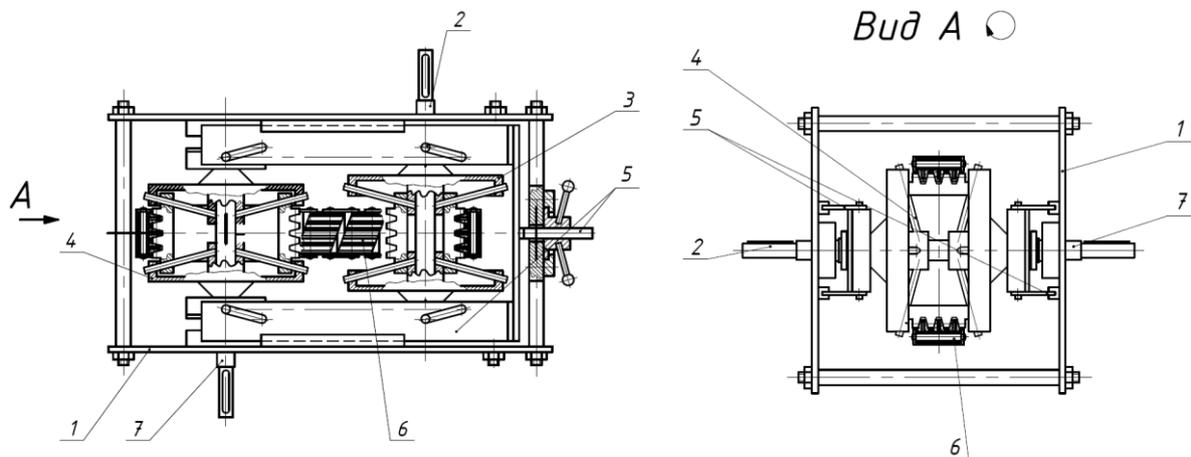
Вариатор с поликлиновым ремнем: 1 – корпус; 2 – ведущий вал; 3 – ведущий составной шкив; 4 – ведомый составной шкив; 5 – механизм регулирования передаточного отношения в виде плоского многопоточного кулачка; 6 – поликлиновой ремень; 7 – ведомый вал
